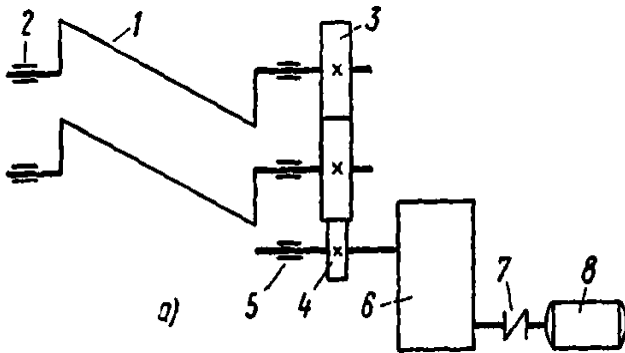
Кінематична схема змішувача із Z-подібними лопатями: 1 – ротор; 2 – підшипникова опора; 3,4 – зубчасті колеса; 5 – додаткова опора; 6 – редуктор; 7 – муфта; 8 – електродвигун
